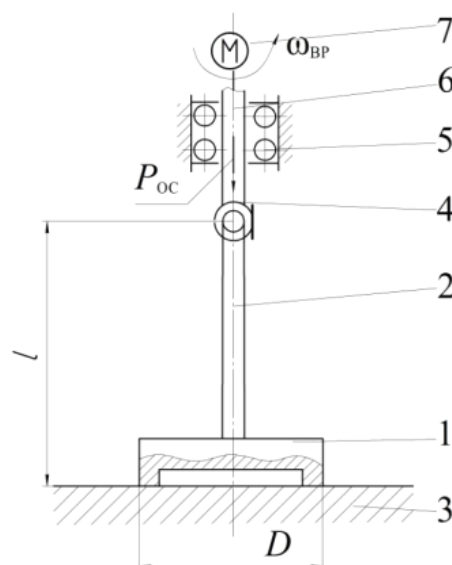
Схема роторного інерційного віброприводу (1 – приводний вал; 2 – підшипники кочення; 3 – опора кочення; D – діаметр тарілки ротора; l – виліт тіла, що обертається)
